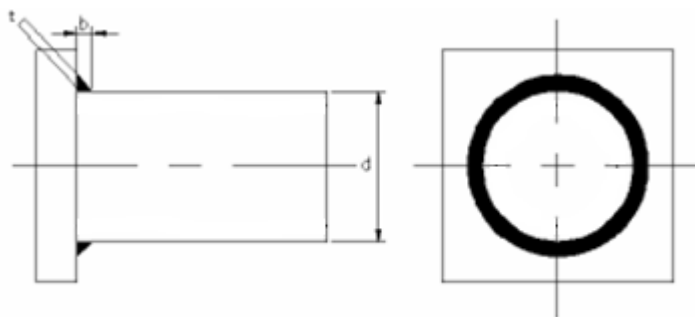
Dimensionamiento de soldadura en Eje
